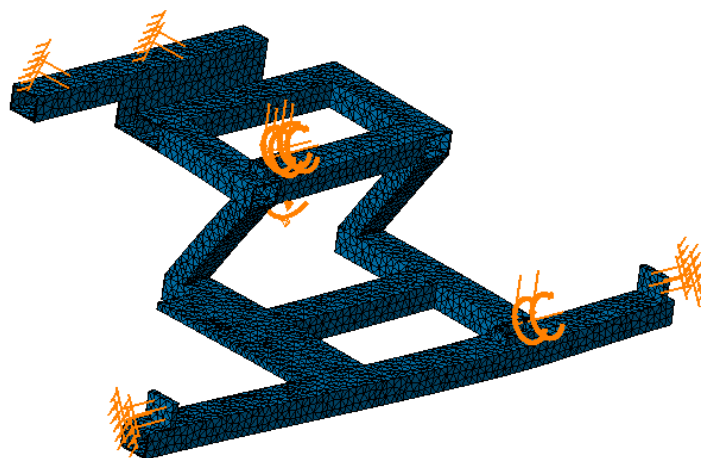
Aplicación de fuerzas y momentos sobre la estructura del estribo.
